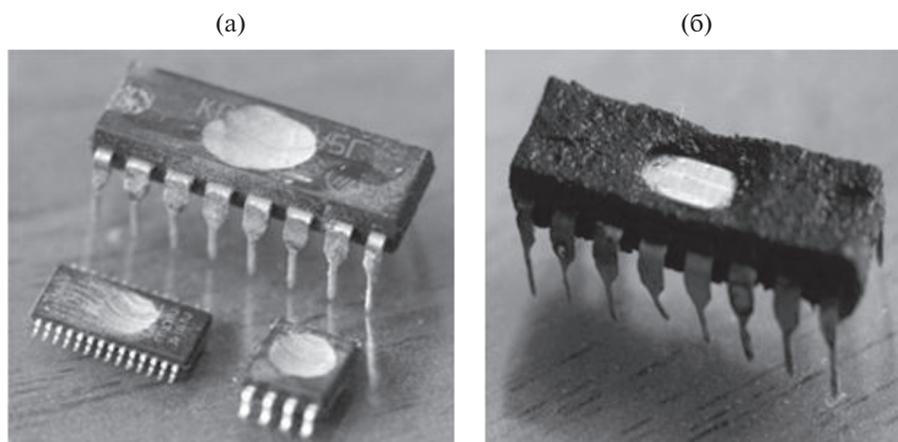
Реинжинеринг микротопологии изделий корпусных ИМС: а – механообработка корпуса; б – химическое травление корпуса.
